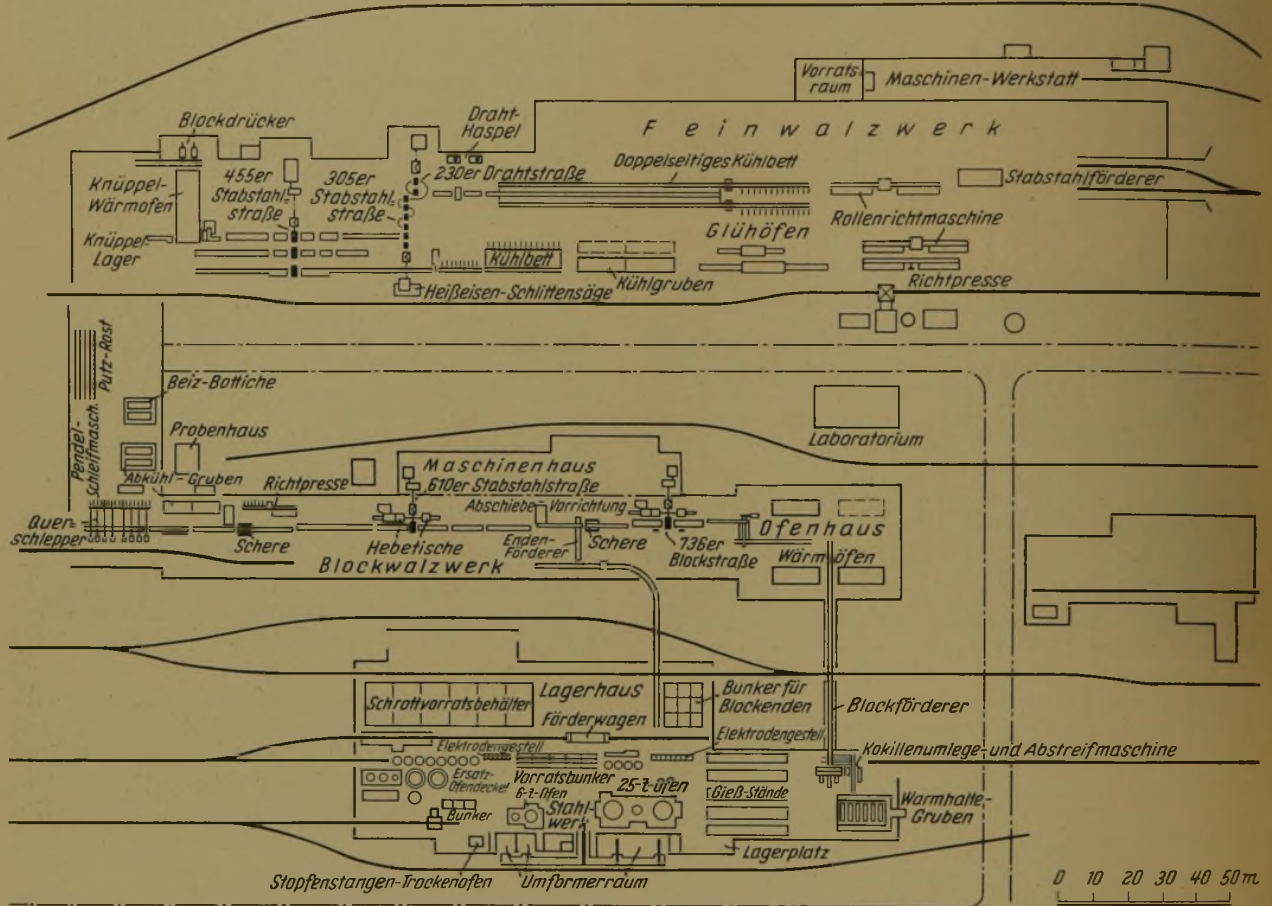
Grundriß des Edelstahlwerks der Copperweld Steel Co., Warren (Ohio).
